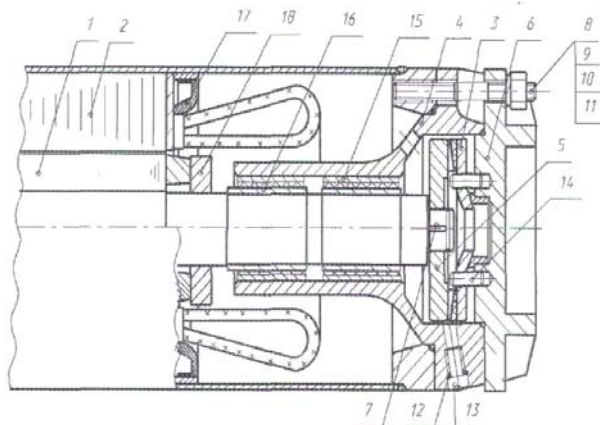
Электродвигатель погружной: 1 – ротор; 2 – статор; 3 – подпятник; 4 – щит подшипниковый; 5 – пята; 6 – днище; 7 – шпонка; 8 – шпилька; 9 – гайка; 10, 11 – шайбы; 12 – кольцо уплотнительное; 13 – пробка; 14 – штифт; 15 – подшипник резинометаллический; 16 – втулка ротора; 17 – кольцо защитное; 18 – кольцо балансировочное из сплава
